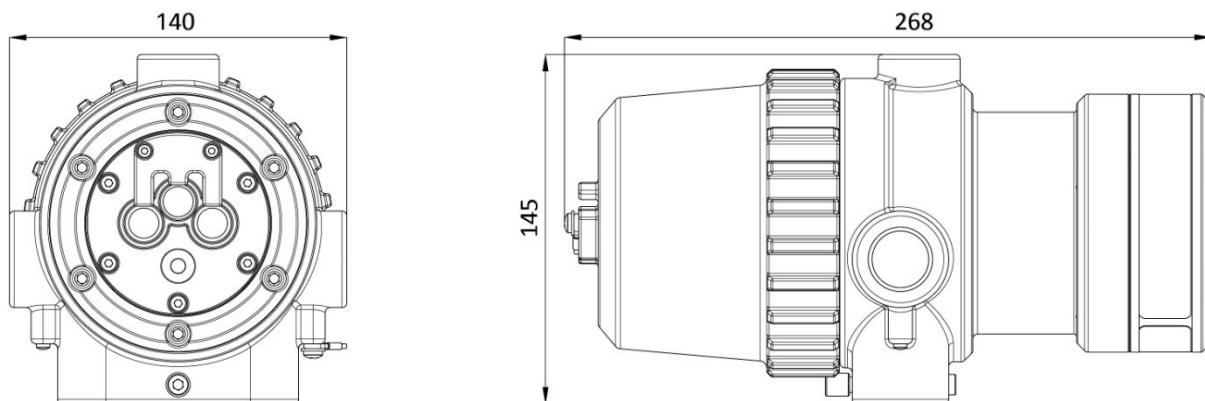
Габаритные размеры извещателя «СПАРК» в мм.
